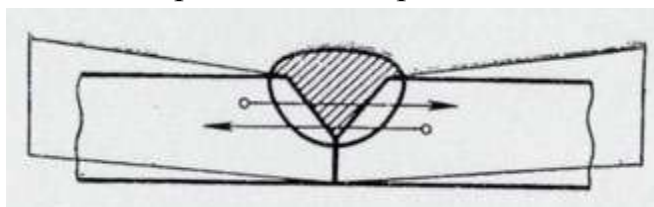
Угловая деформация при сварке стыкового соединения.
